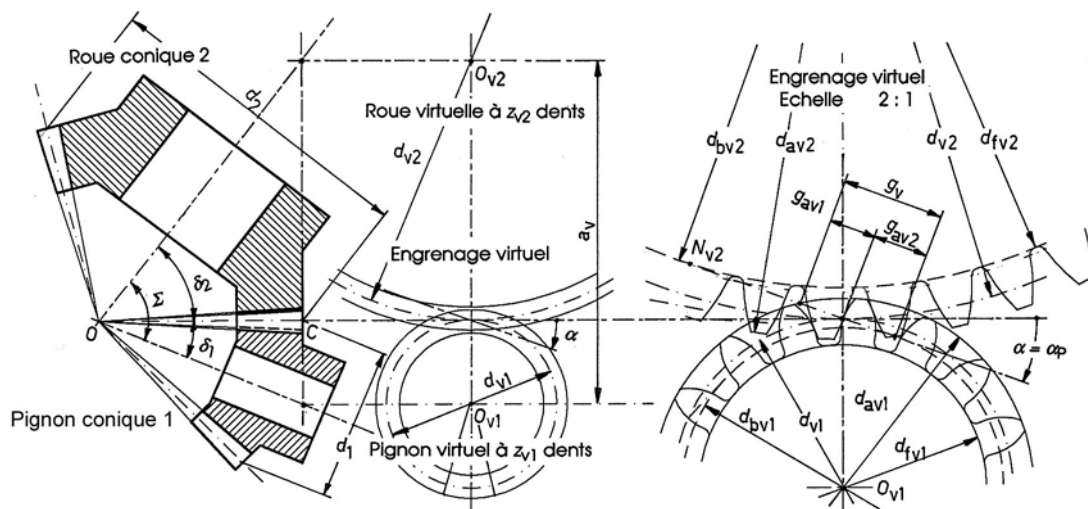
Engrenage conique : roues virtuelles et engrenement de ces roues
